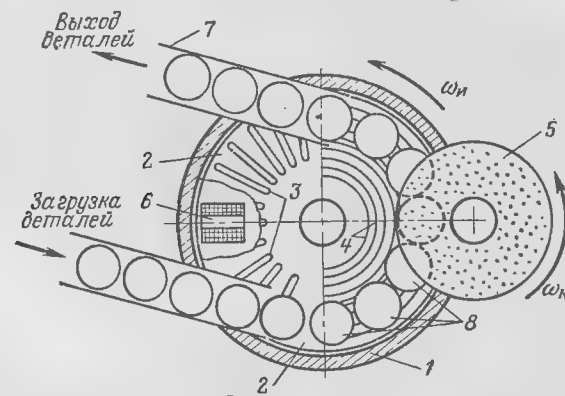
Поворотный электромагнитный стол с непрерывной загрузкой деталей.
